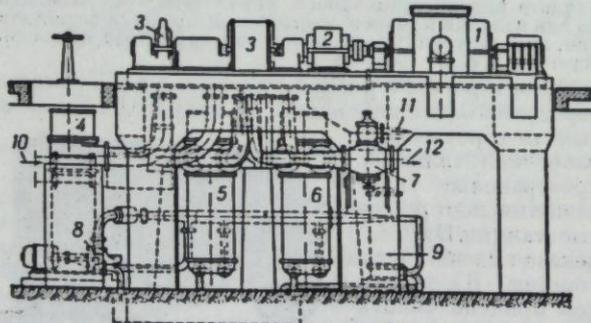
Компрессорная установка: 1 — электродвигатель; 2 — редуктор; 3 — корпус турбокомпрессора; 4 — охладитель воздуха первой ступени; 5 — охладитель воздуха второй ступени; 6 — охладитель воздуха четвертой ступени; 7 — обратный клапан; 8 — насос для подачи воды; 9 — охладитель масла; 10 — место васа воздуха; 11 — выход воздуха в атмосферу; 12 — выход воздуха в напорный воздухопровод.
